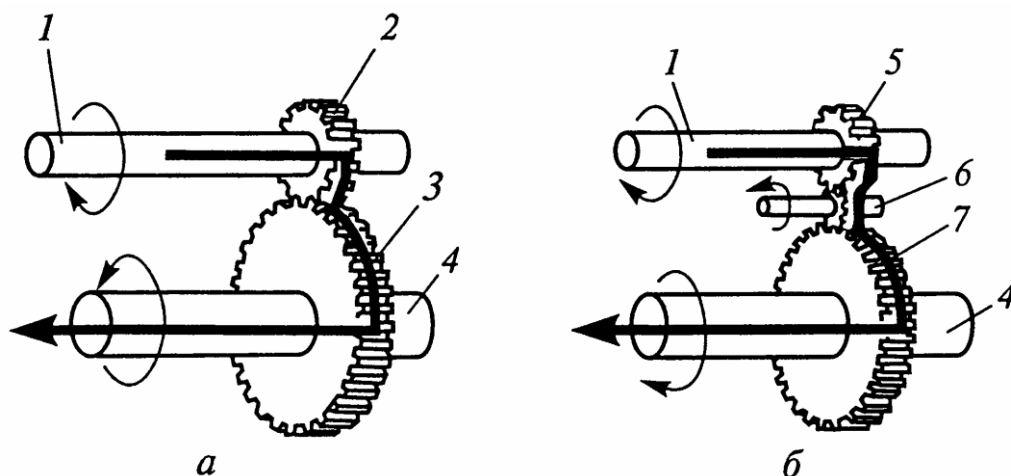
Схема роботи двохвальної коробки передач: *а* – рух вперед; *б* – рух заднім ходом; 1 – первинний вал; 2, 3, 5, 6, 7 – шестерні; 4 – вторинний вал
